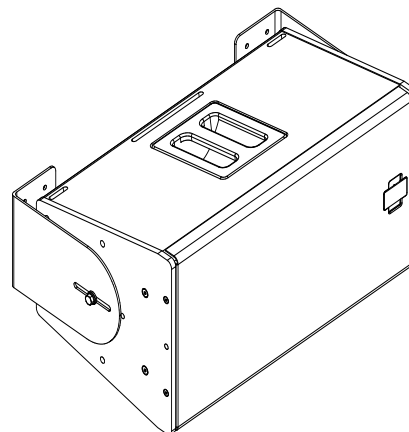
Montaje horizontal del UPJ-1P en muros
